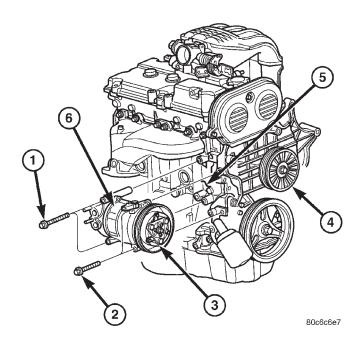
COMPRESOR DE A/A - MOTOR 2.4L
